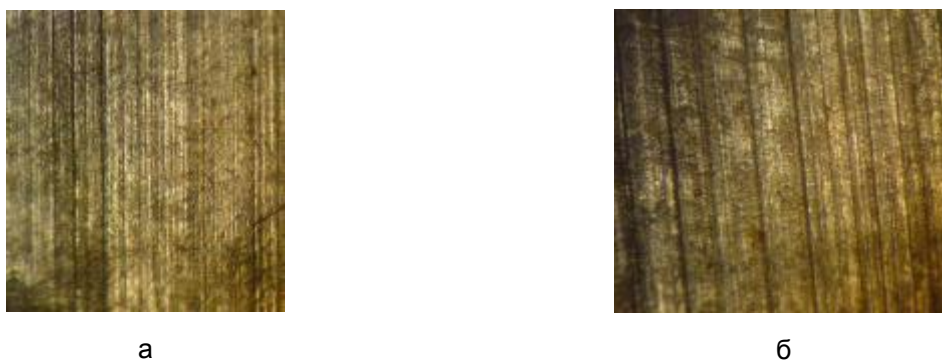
Образцы поверхности при увеличении в 100 раз (попутное фрезерование)
